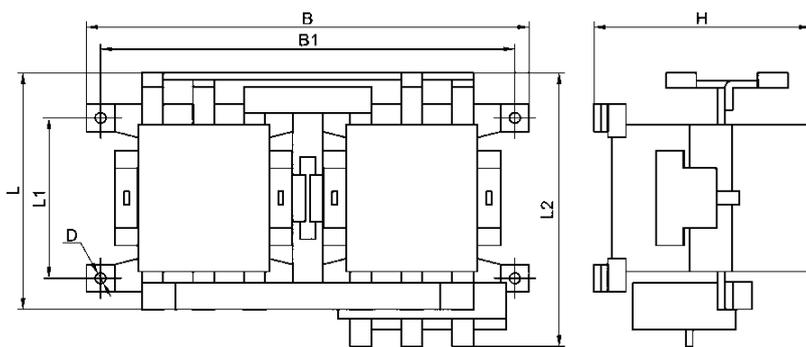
Пускатель реверсивный ПМА-5000, ПМА-6000, IP00
